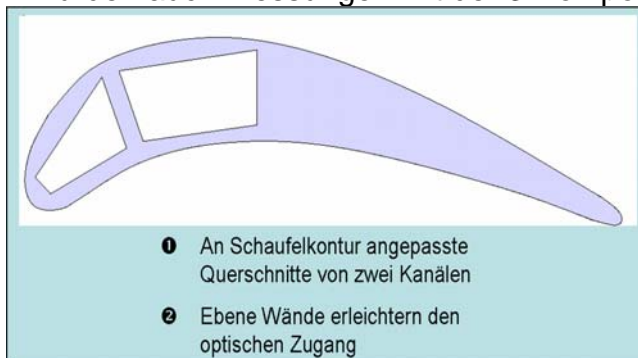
Multipass-Kühlsystem einer Rotorschaukel Bild 2 Stereo-PIV am Kühlsystem
